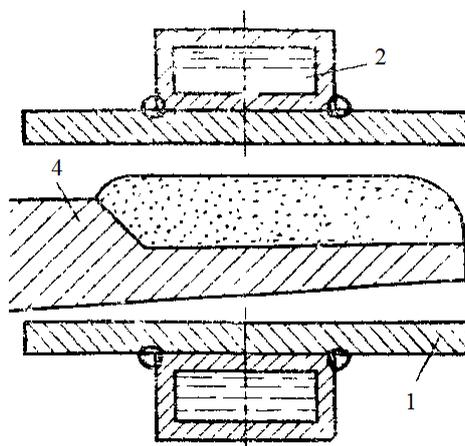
Схема индукционной наплавки, где 1-индуктор, 2-вода для охлаждения индуктора, 3-наплавочный материал, 4-наплавляемая деталь
